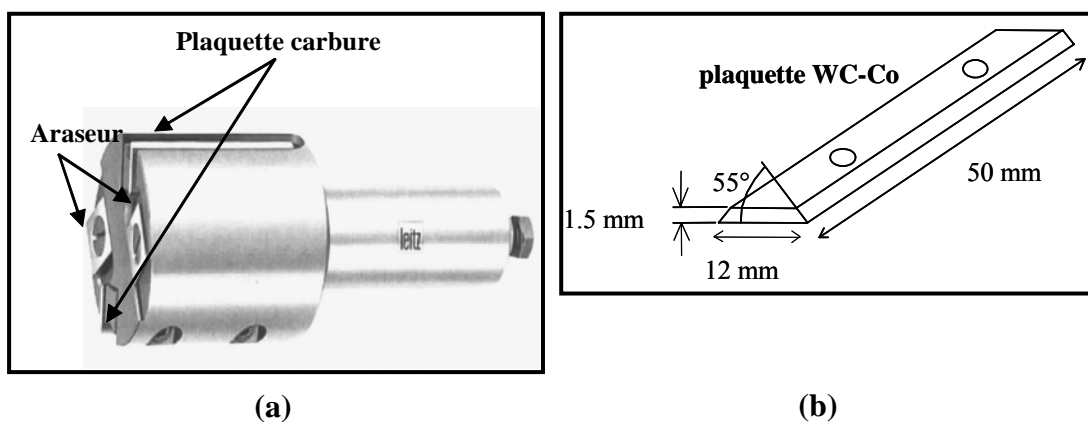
(a) outil de fraisage (défonçage), (b) géométrie des plaquettes carbures
